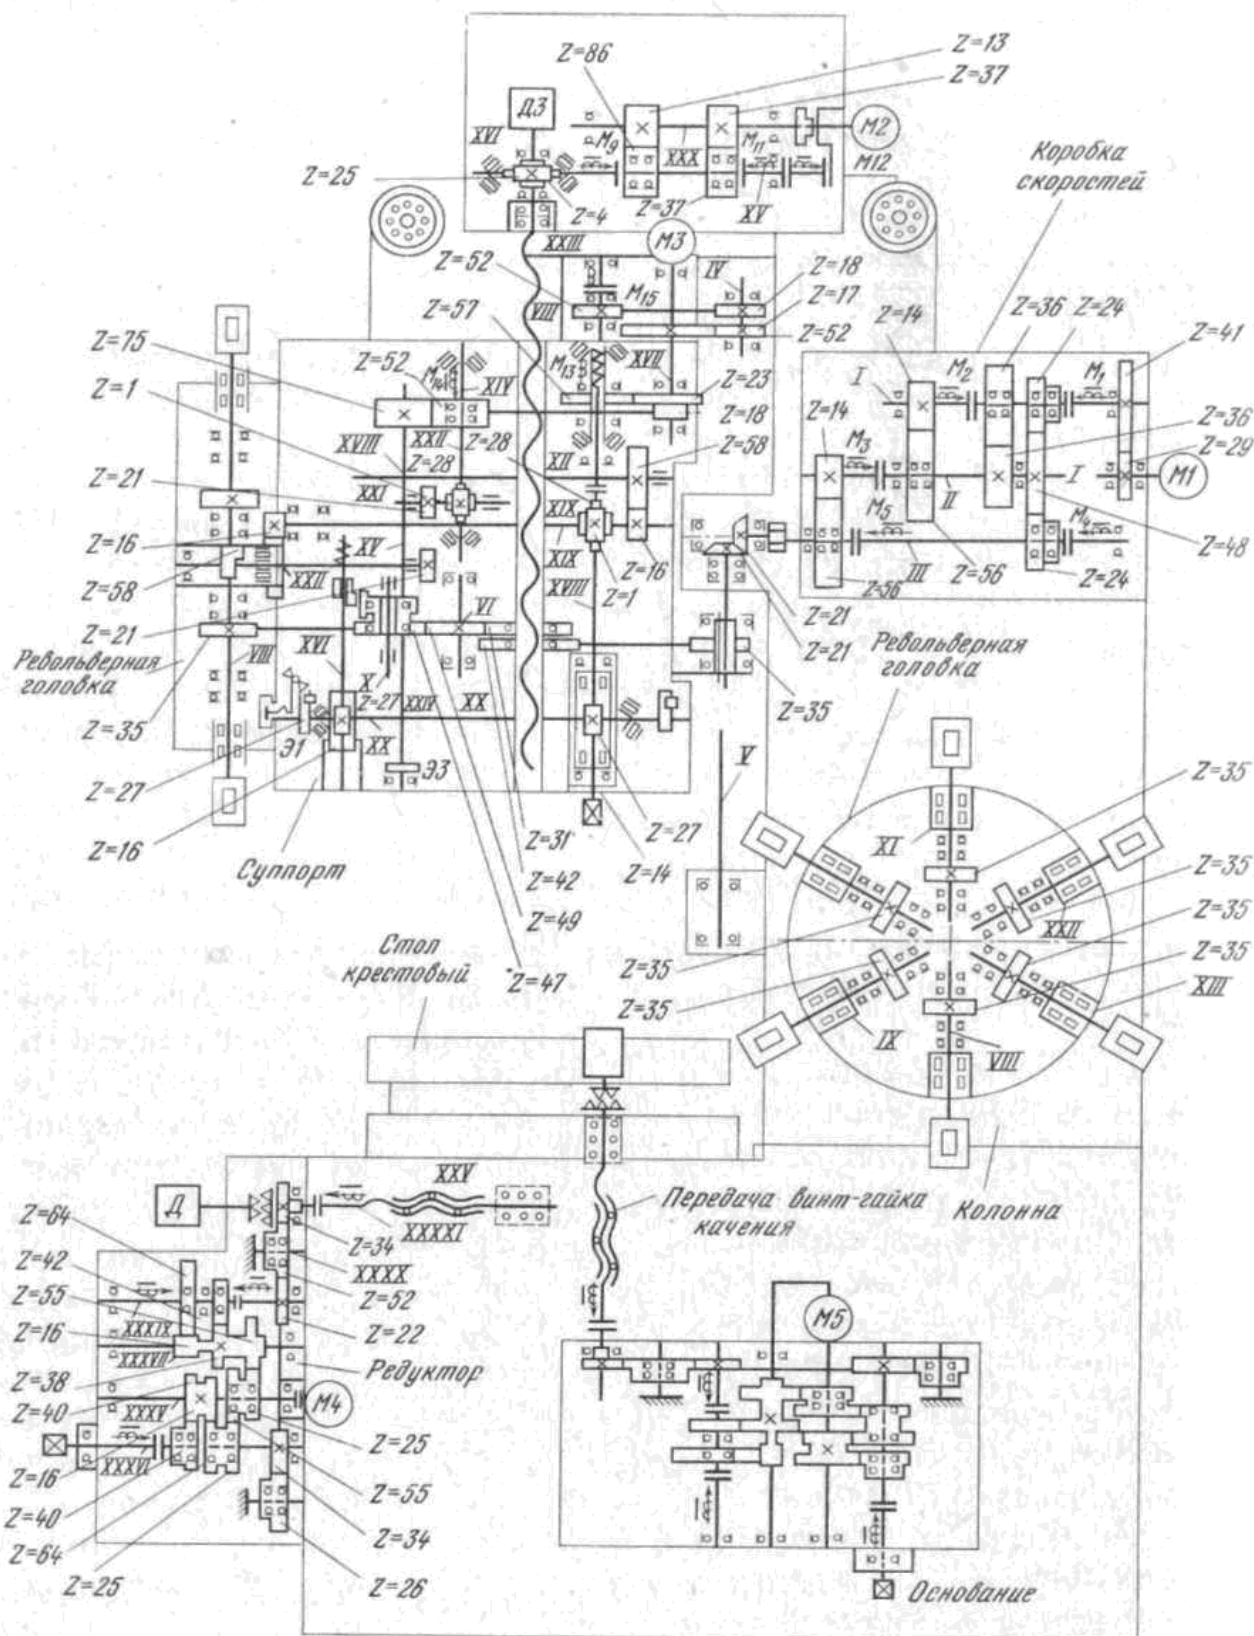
Кинематическая схема станка 2P135Ф2-1.
